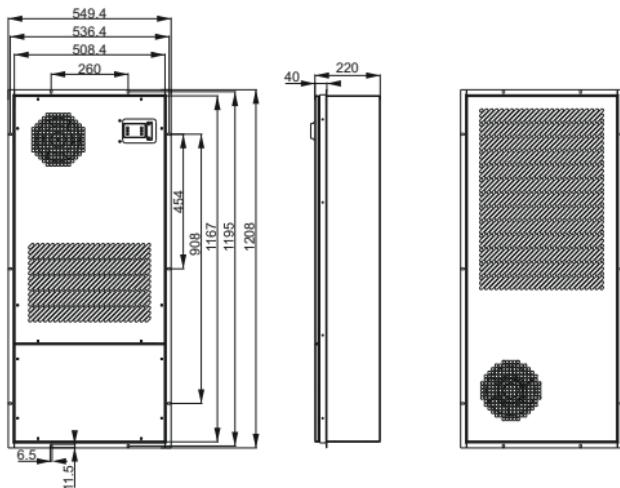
Внешний вид и габаритные размеры моделей СМ-3000-230 и СМ-3500-230 / Figure 5 – Appearance and overall dimensions of CM-3000-230 and CM-3500-230 versions
